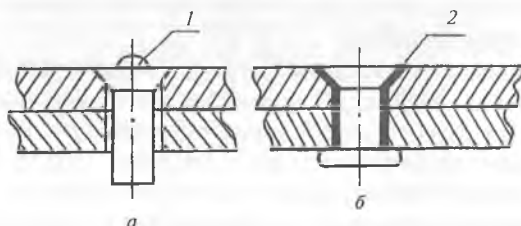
Заклепка с компенсатором: а — конструкция заклепки; б — расклепанная заклепка; 1 — компенсатор; 2 — зона упрочнения материала
